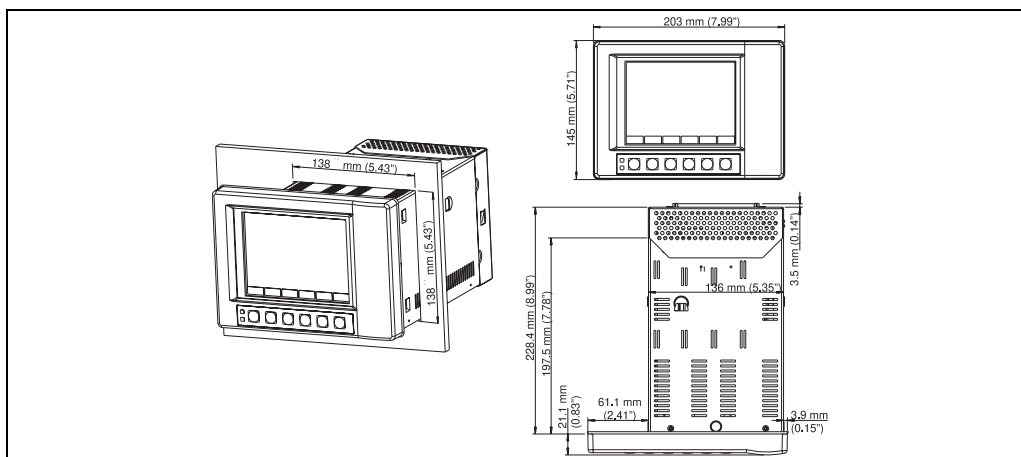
Montaje en panel de la versión con fundición inyectada o de acero inoxidable
